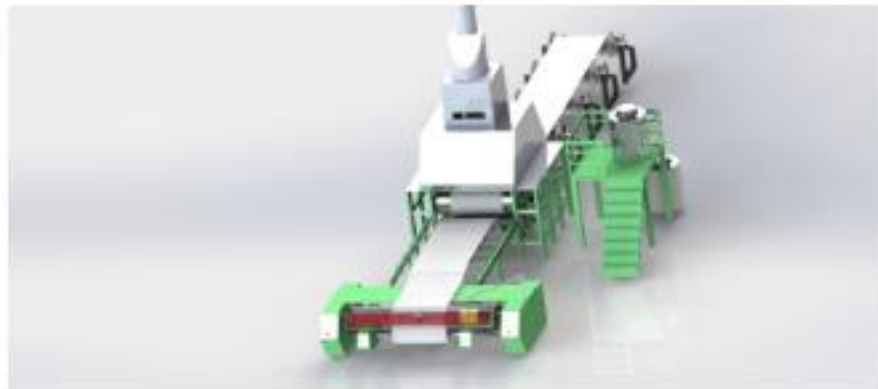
Diseño CAD de la máquina engomadora Zell.
